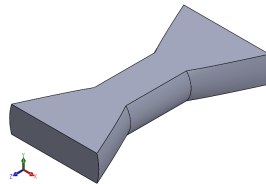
Llave de unión entre la cubierta y la carcasa.
